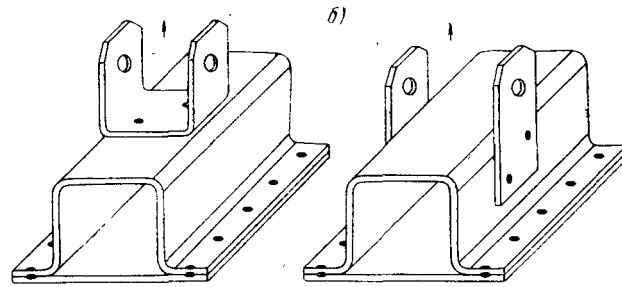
Детали, сваренные точечной сваркой:
